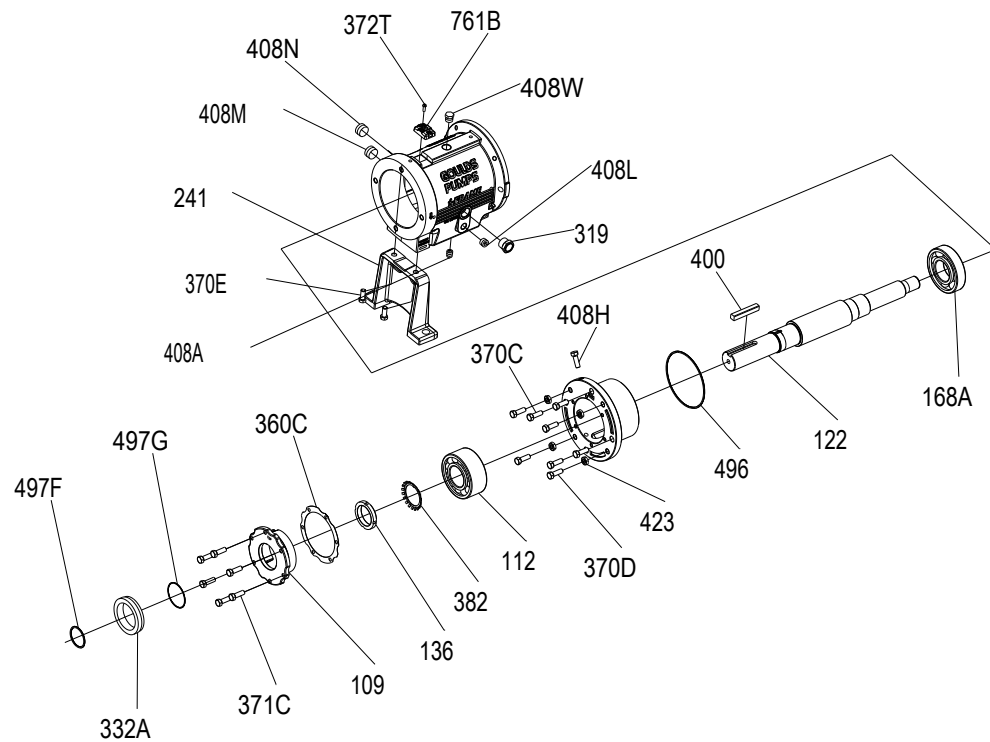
XLT-i-Stützschaale Explosionszeichnung
